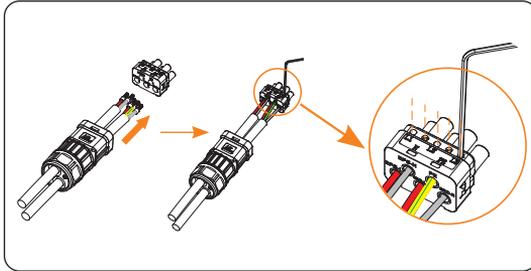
Die gecrimpten Kabel einfädeln
